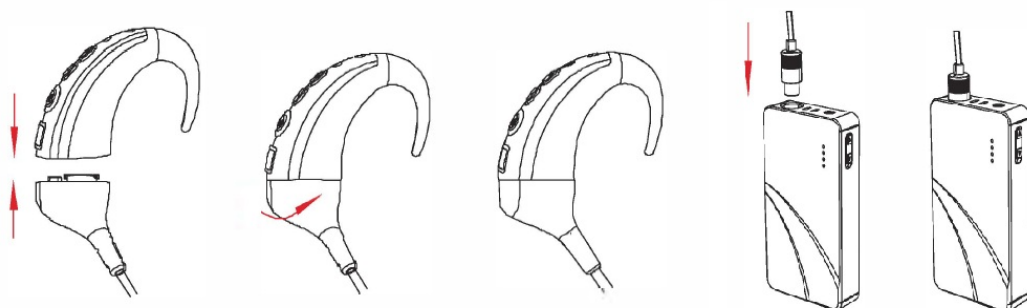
Сборка речевого процессора и аккумуляторного блока питания для НТН
